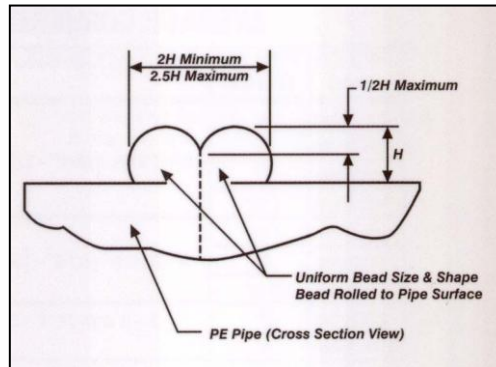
Dimensiones que debe presentar el cordón de soldadura.
